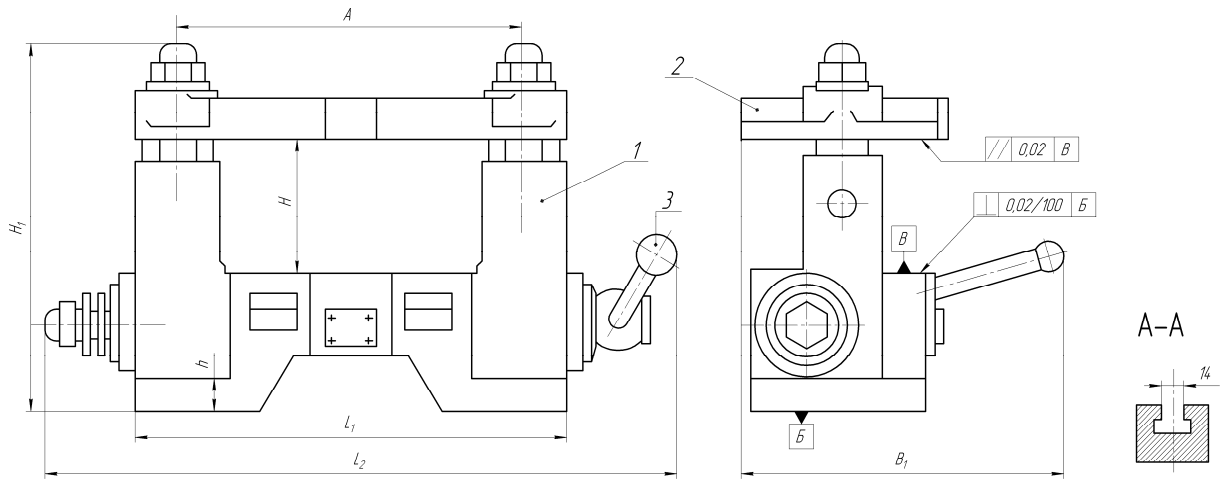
Будова й параметри кондуктора для свердління отворів у болтах, шпильках і валиках: 1 – шпилька; 2 – ексцентрик; 3 – болт; 4 – корпус; 5 – колодка
